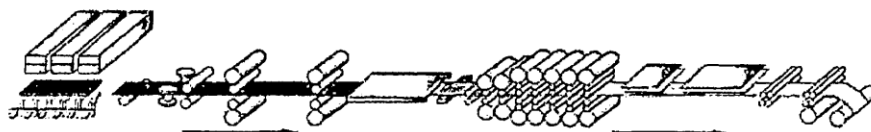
Схема процесса изготовления горячекатаной стали
